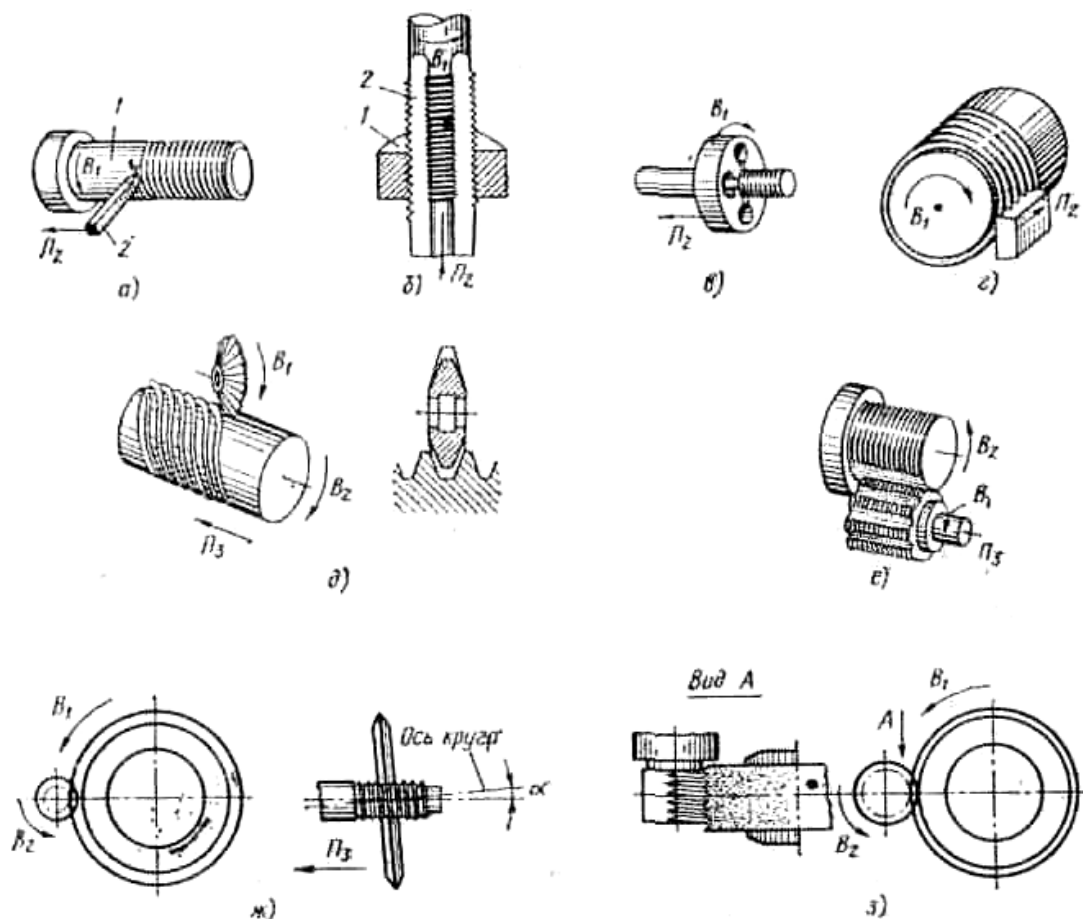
Формообразование винтовых поверхностей на заготовках 1 режущим инструментом 2
